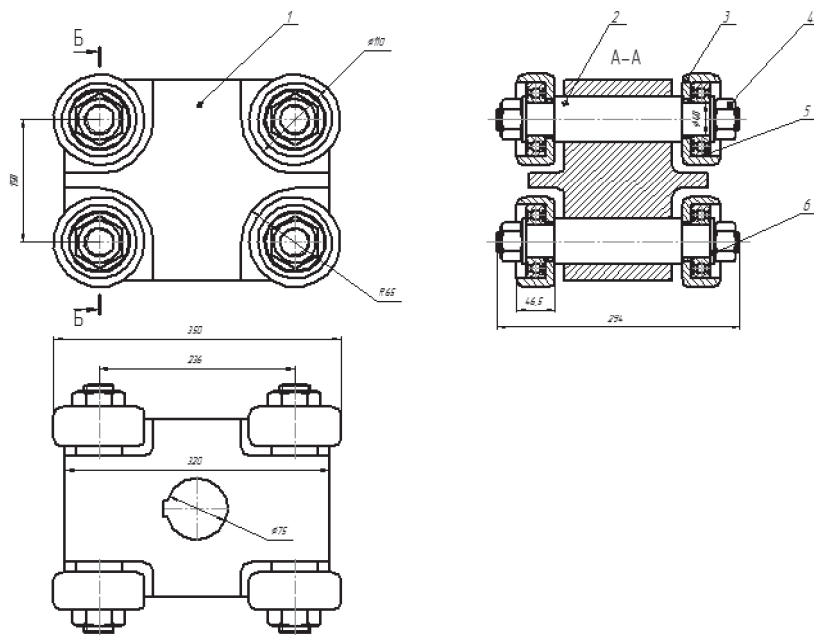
Каретка: 1 – корпус; 2 – ось; 3 – ролик; 4 – гайка;
